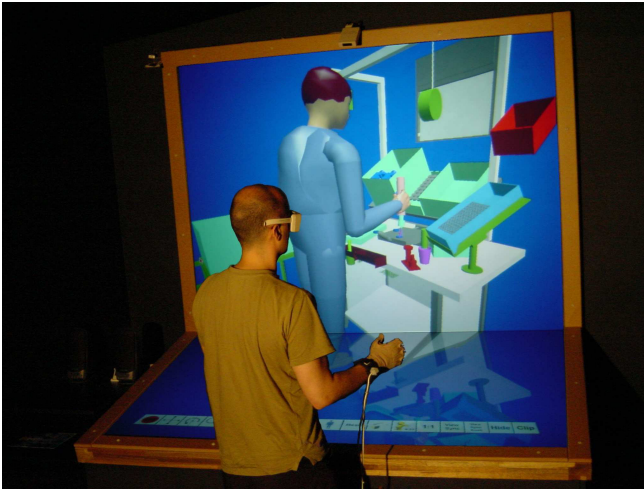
Schraubwerkzeug wird in Position zur Montagestelle gebracht
